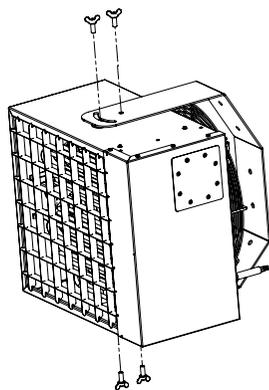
Схема монтажа тепловентилятора на кронштейн
